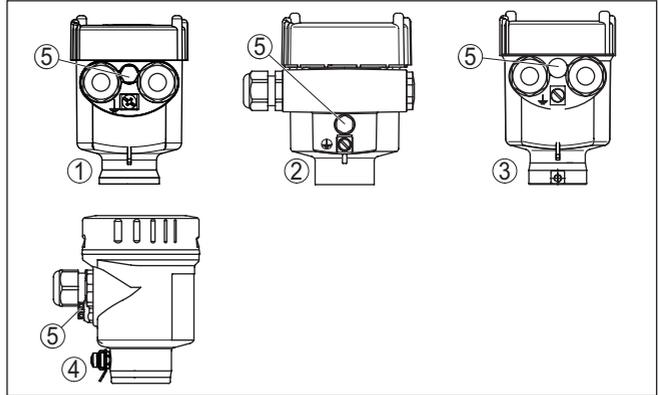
Однокамерний корпус із різноманітних матеріалів
